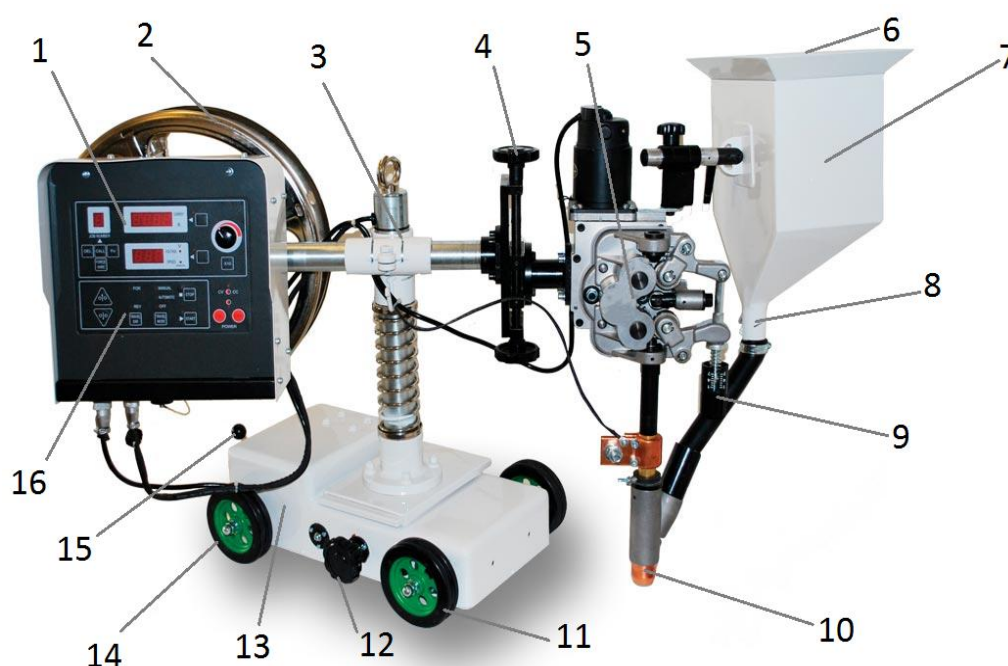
Сварочный трактор Pandaweld 1250:
